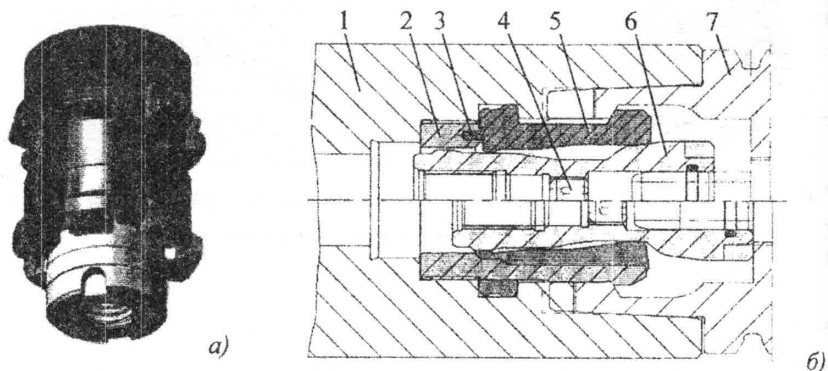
Цанговый механизм захвата хвостовиков HSK с дополнительной цангой фирмы Röhrl Spannzeuge: а) общий вид; б) конструкция
